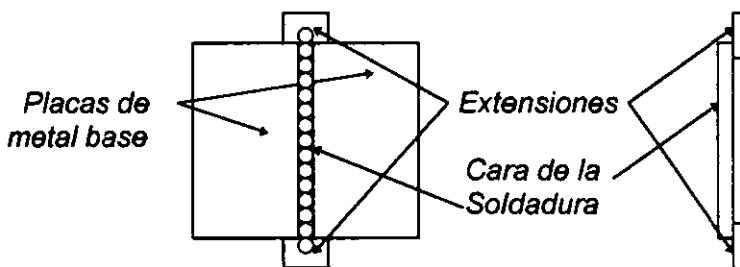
Extensiones para dar continuidad a las soldaduras.
